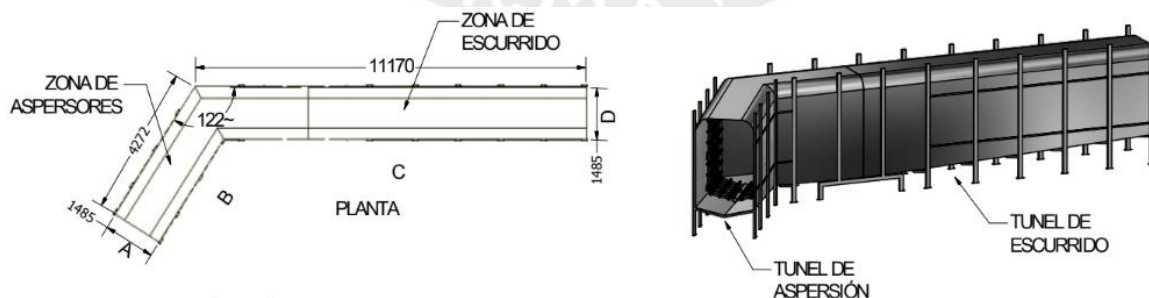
Vista de planta e isométrica del túnel de pre-tratamiento. (Matransa, 2018)
